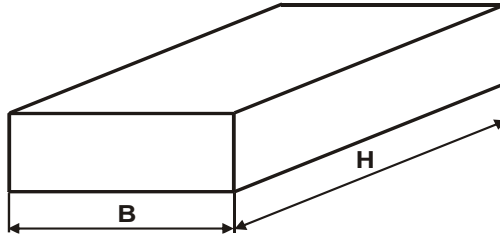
Загальний вигляд оброблюваного зразка
